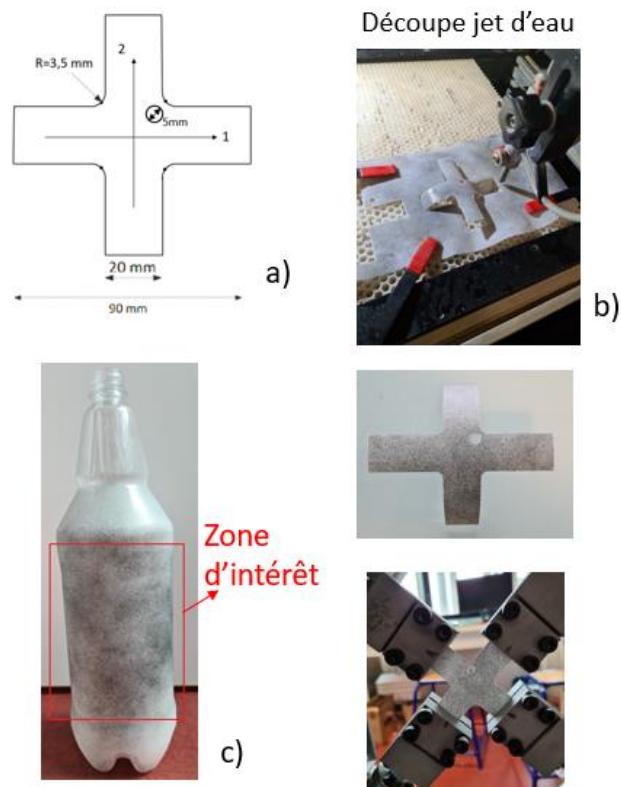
Procédure de découpe des éprouvettes bi-axiales a) Schéma de l'éprouvette, b) Eprouvette découpée par jet d'eau et installation de l'éprouvette sur le banc de traction bi-axial, c) Zone de prélèvement de l'éprouvette d'une bouteille
